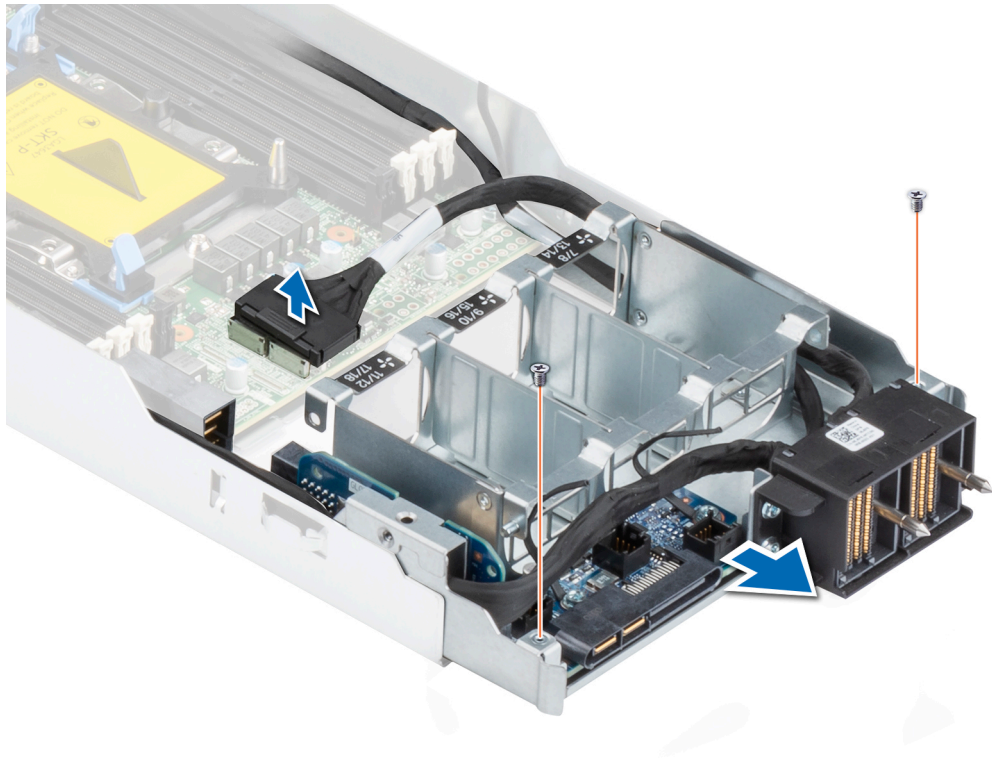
Entfernen des Motherboard-Brücken-Moduls
